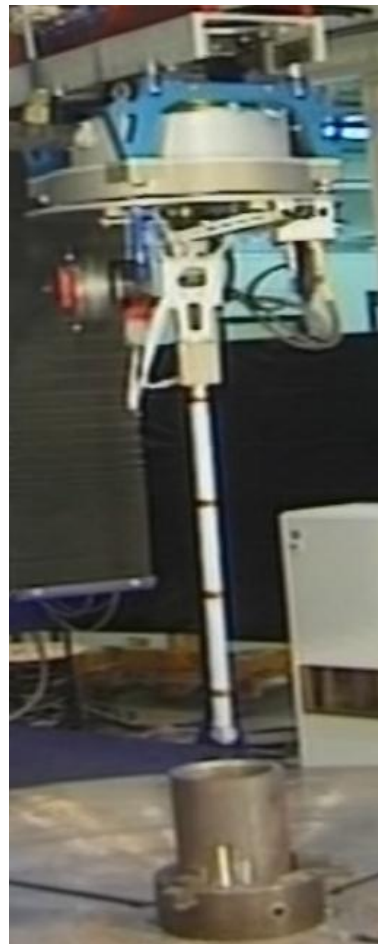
Узел приварки патрубков СУЗ к крышке ВБ установки В-320
